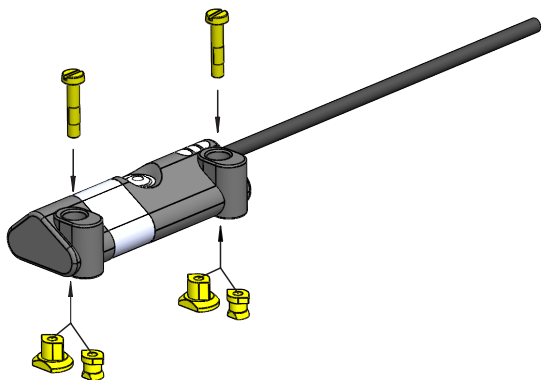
Montaggio nottolini a T (a sinistra) o nottolini a C (a destra)
